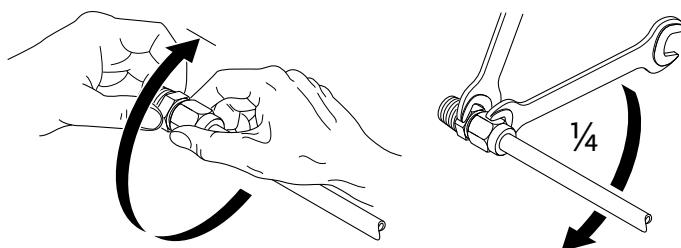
Дополнительный поворот резьбового соединения с обжимным кольцом на 1/4 оборота
